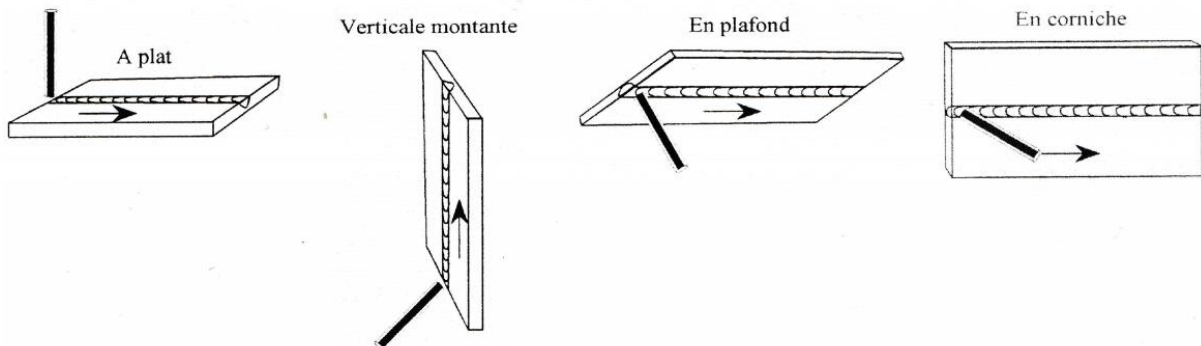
Positions de soudage pour les soudures bout à bout (SAF 1995).
